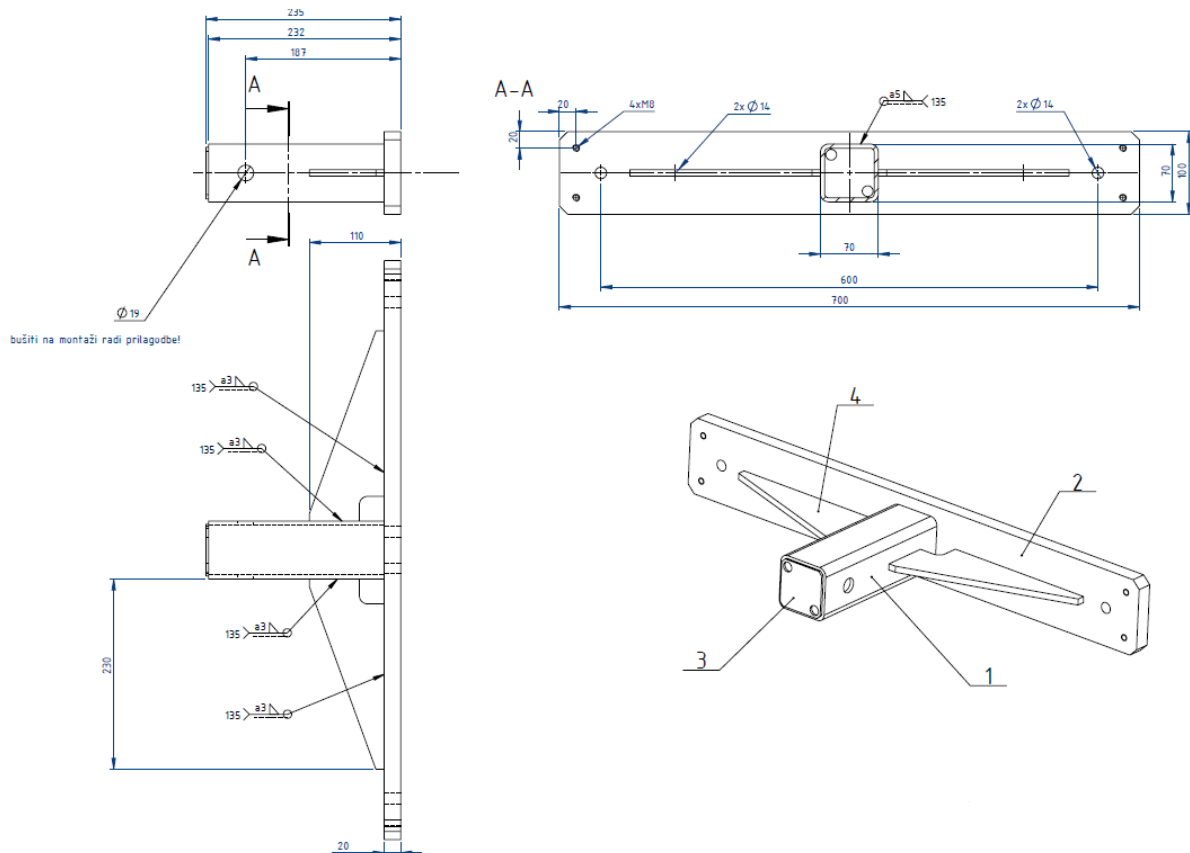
Parametri kod zavarivanja stupa konstrukcije
